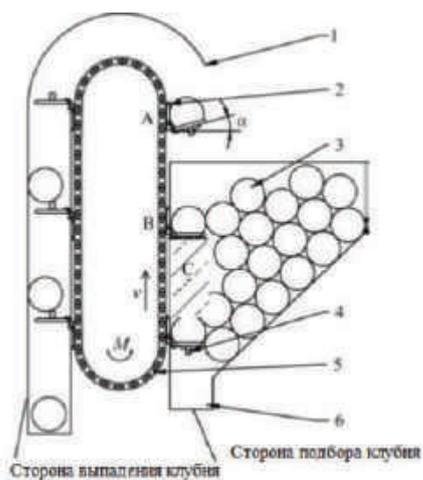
Схема высаживающего аппарата картофелесажалки цепочно-чашечного типа: 1 – шахта; 2 – цепь; 3 – клубни картофеля; 4 – чашечка для клубней; 5 – приводная цепь; 6 – бункер
